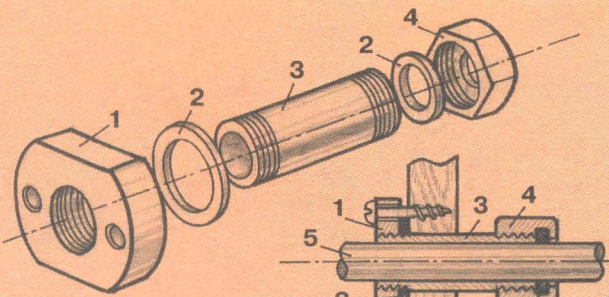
Втулка вала винта: 1 — крепежная шайба; 2 — резиновая прокладка; 3 — втулка; 4 — накидная гайка; 5 — вал винта.
